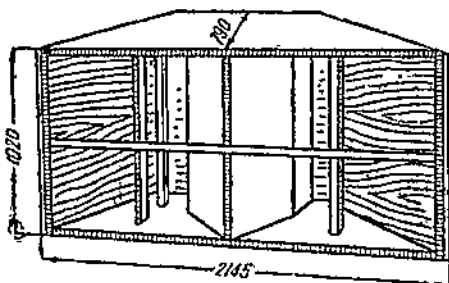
Рупор низкочастотный деревянный типа РНД-2
